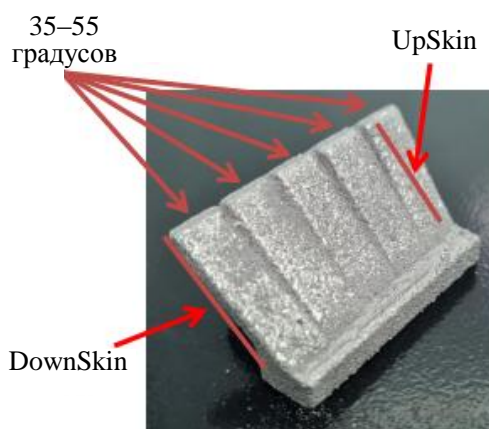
Специальный образец для измерения шероховатости с поверхностями UpSkin и DownSkin
